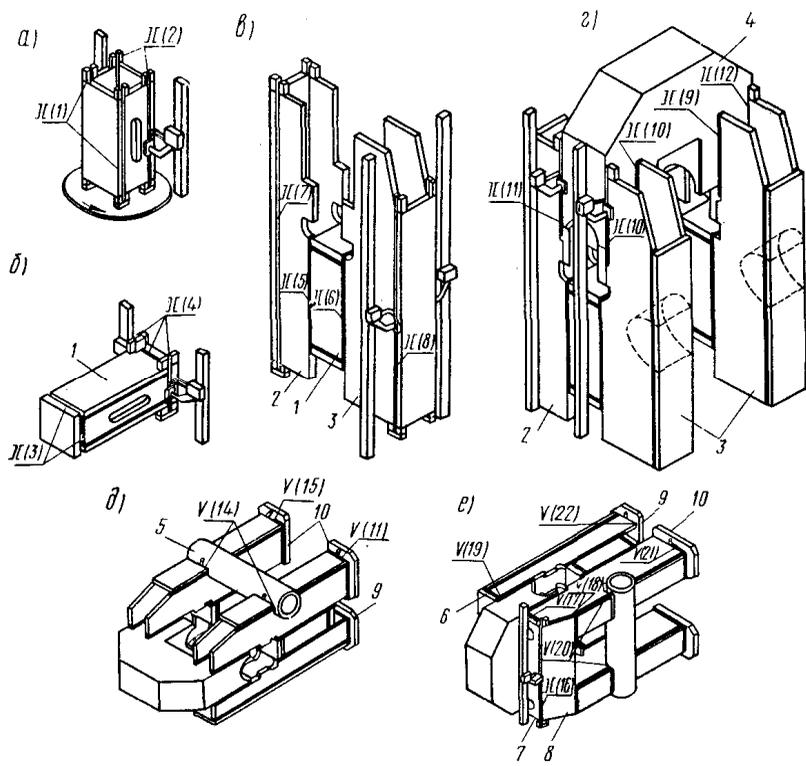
Последовательность сборочно-сварочных операций при изготовлении станины пресса
